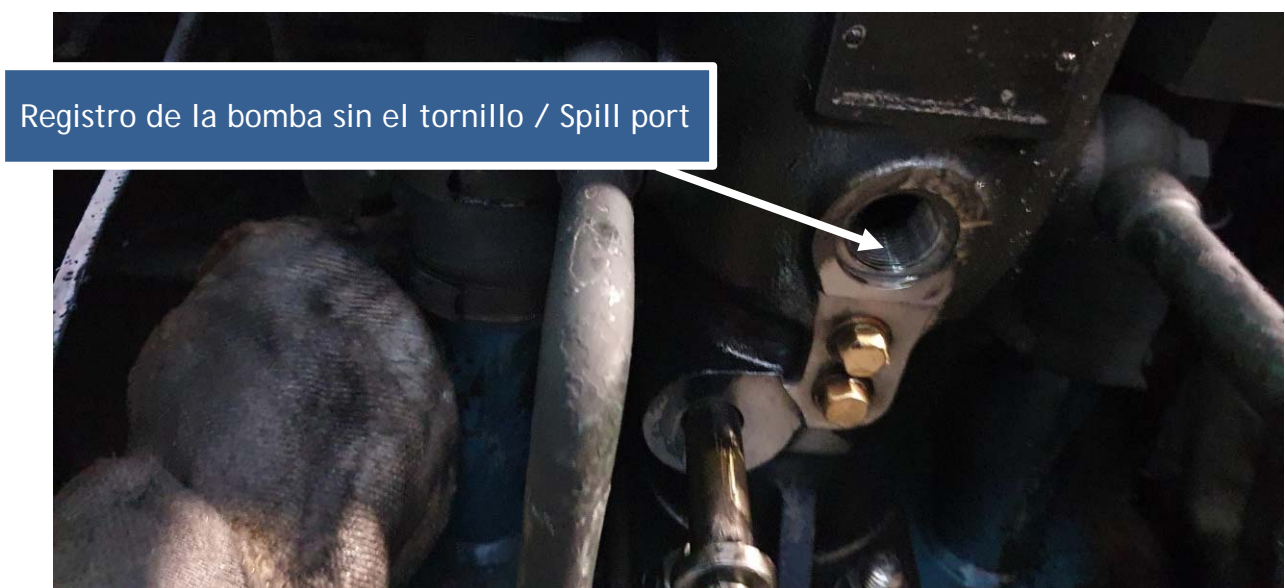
Detalle del frontal de la bomba de combustible sin el "Spill plug"
